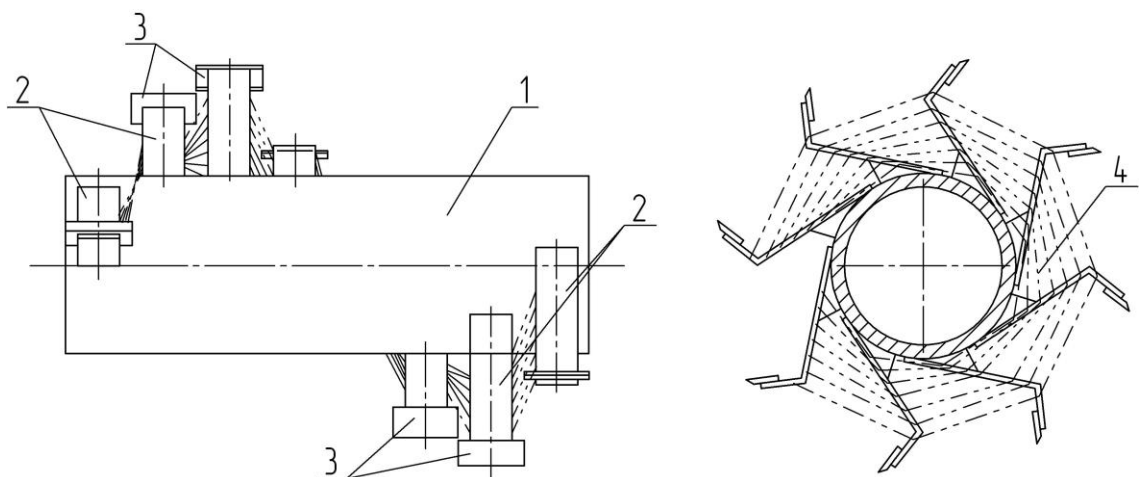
Різально-метальний робочий орган із дотичними зубами.
